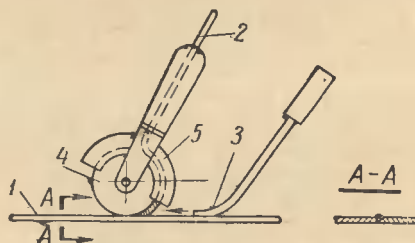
Ролик для прикатки сварочного прутка.
